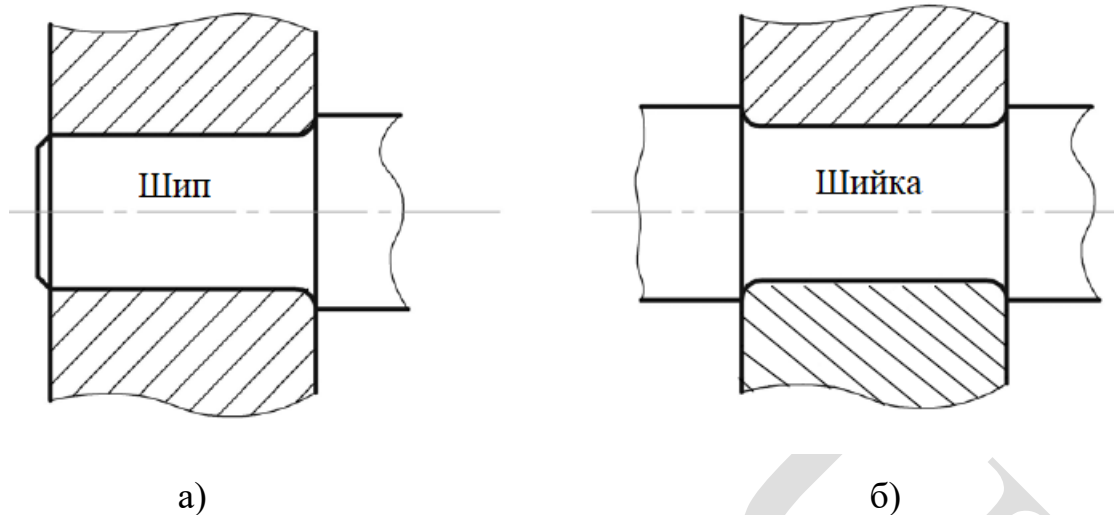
Форма робочої поверхні підшипника ковзання: а – шип, б – шийка
